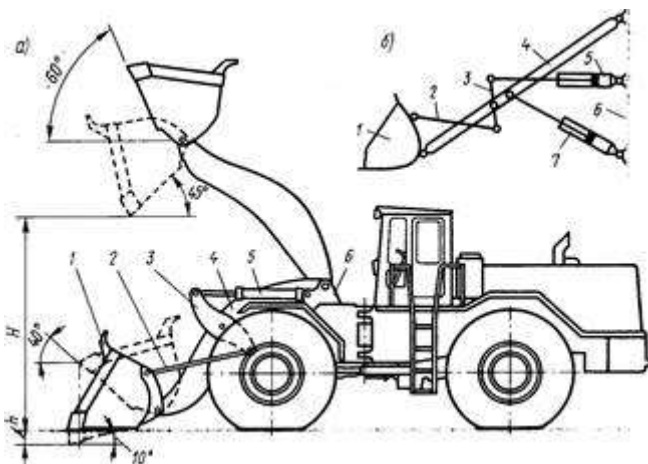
Одноковшовый фронтальный погрузчик: а—схема конструкции; б—кинематическая схема погрузочного оборудования
